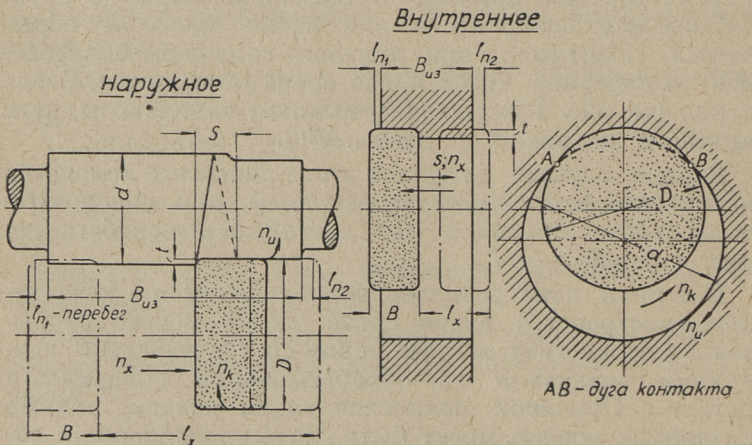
Продольное шлифование круглое наружное и внутреннее.
